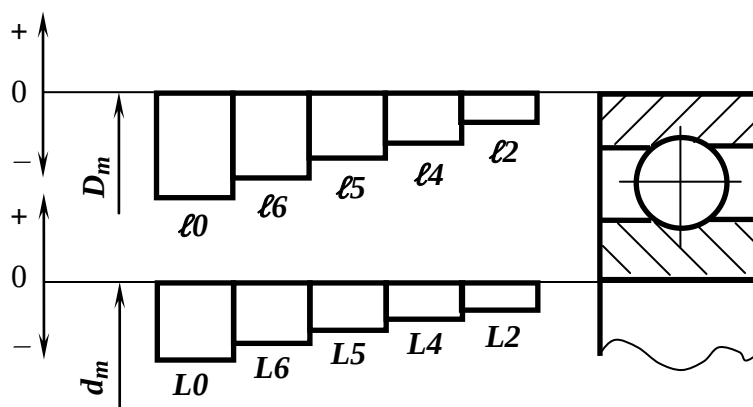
Схема расположения полей допусков диаметров d_m и D_m колец подшипников качения разных классов точности
